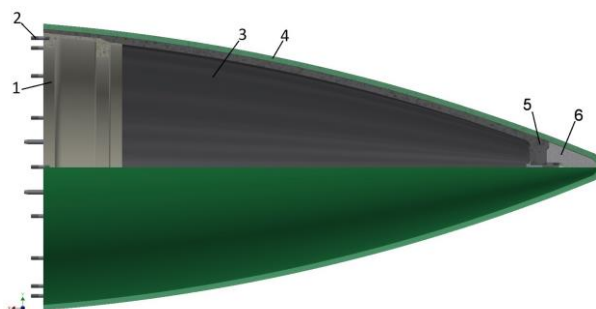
Обтекатель с обечайкой из стеклопластика: 1 – торцевой шпангоут; 2 – резьбовая шпилька; 3 – стеклопластиковая обечайка; 4 – теплозащитное покрытие; 5 – шпангоут; 6 – наконечник
